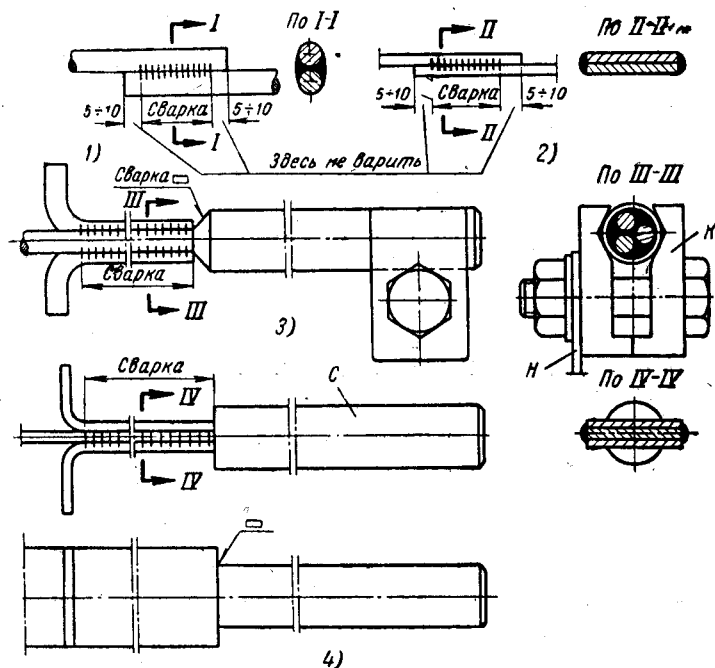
Сварка нагревательных элементов и приварка выводов.
